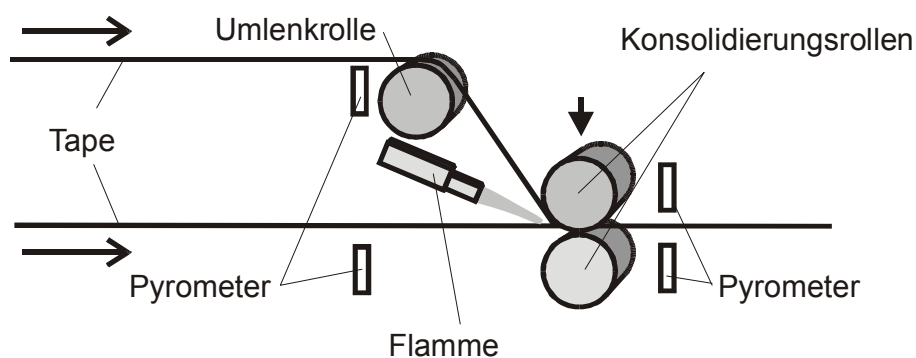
Aufbau zum Verschweißen von zwei Tapes mit Flammheizung
